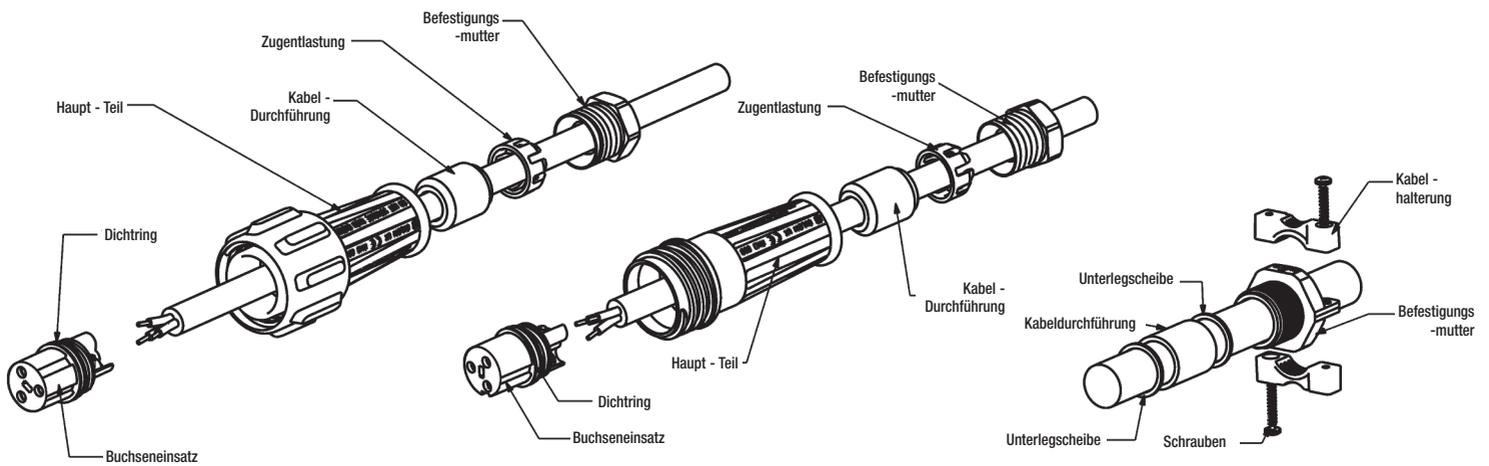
Befestigung Kabelverbinder (PX0910, PX0911)
